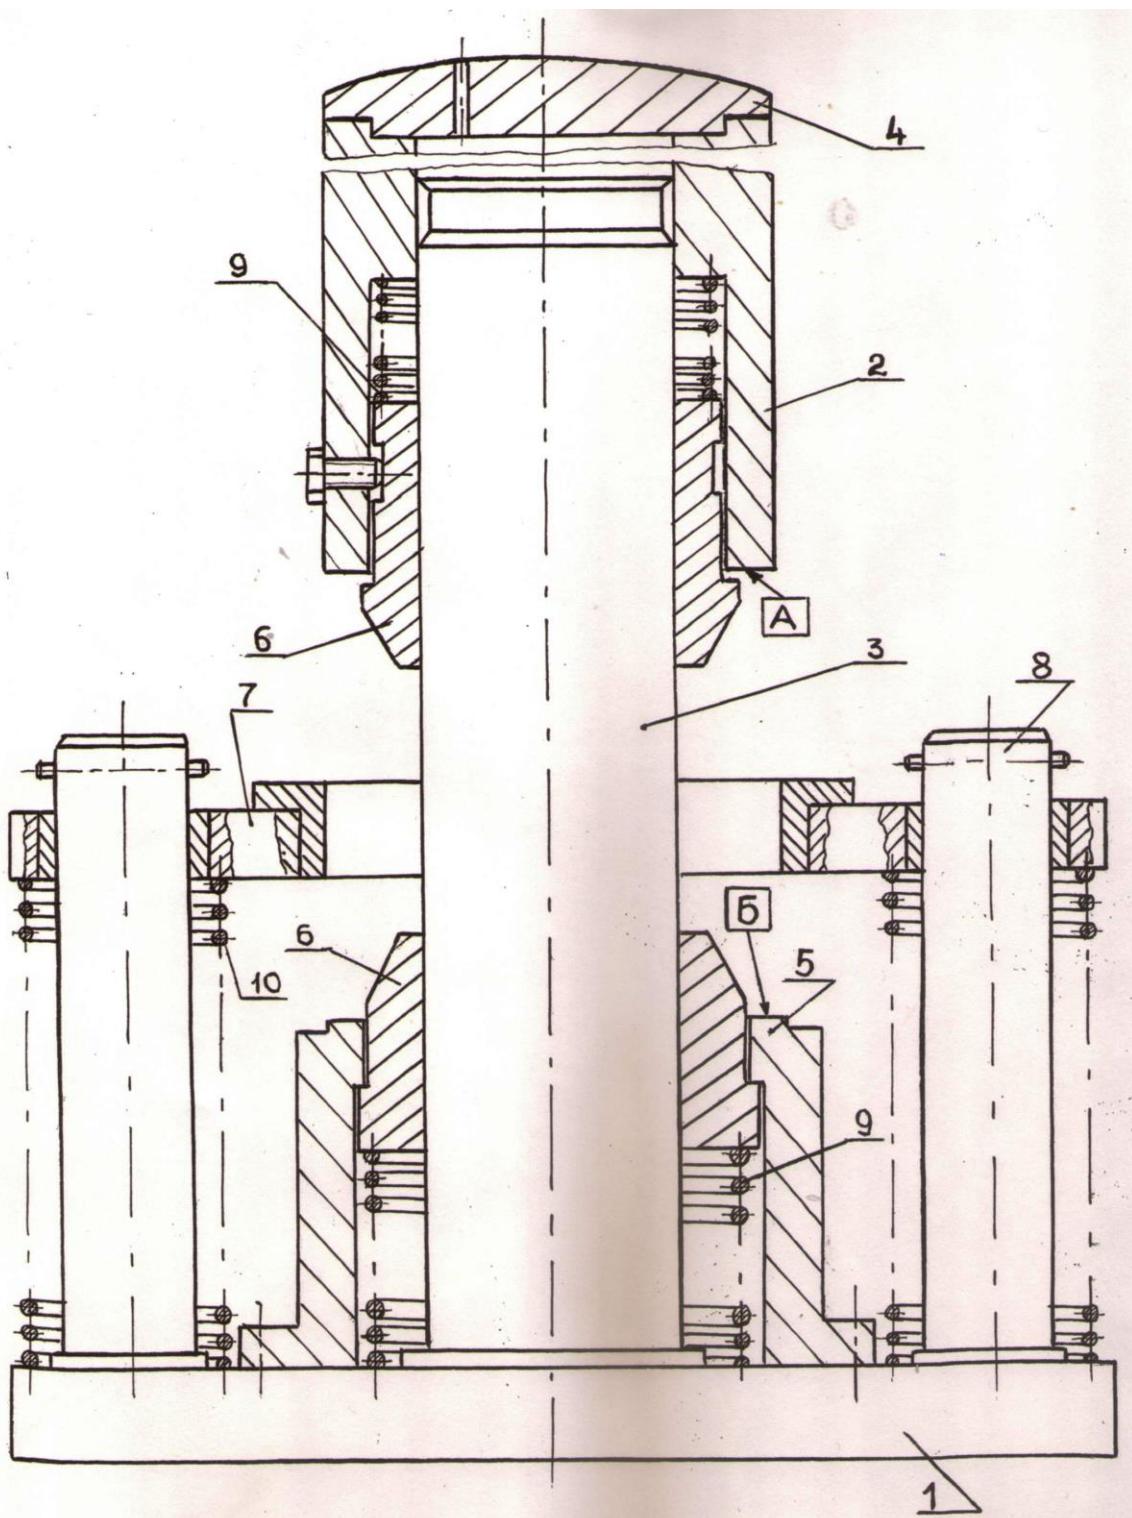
Установка для запрессовки наружных колец дуплекса конических ПК.
